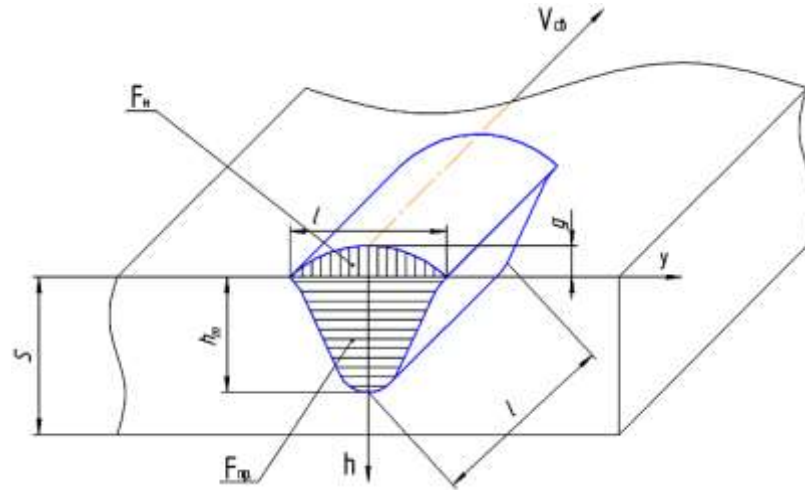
Геометрические параметры зоны проплавления при автоматической сварке под флюсом
